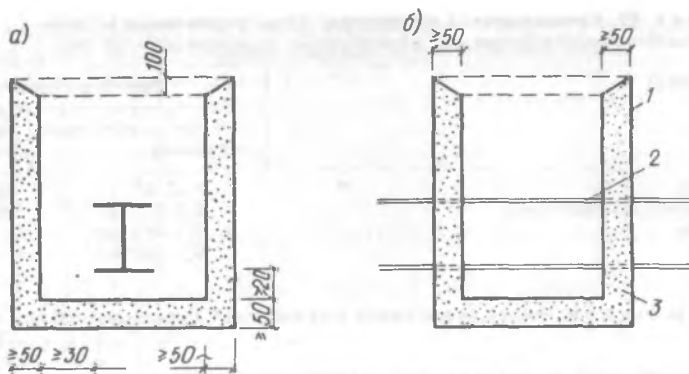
Схема изготовления формы с облицовкой (опоки) для термитной резки
